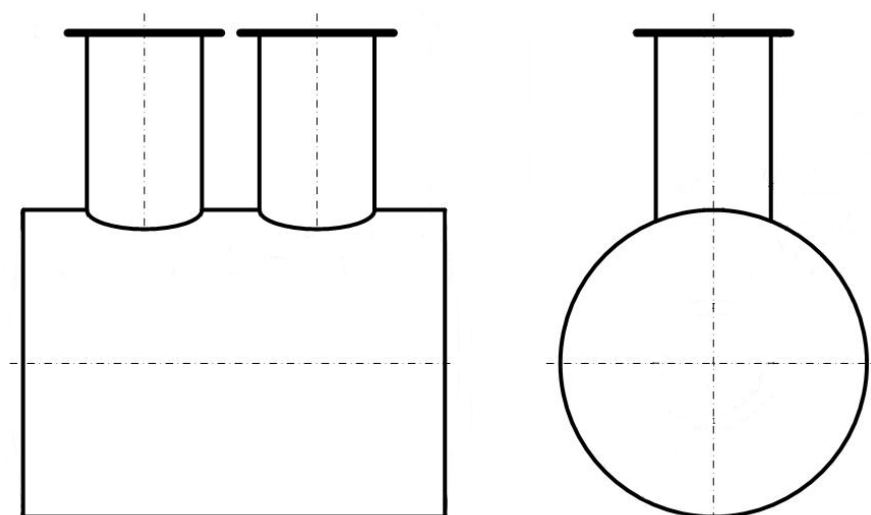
Общий вид эскиза резервуара РГС-25
